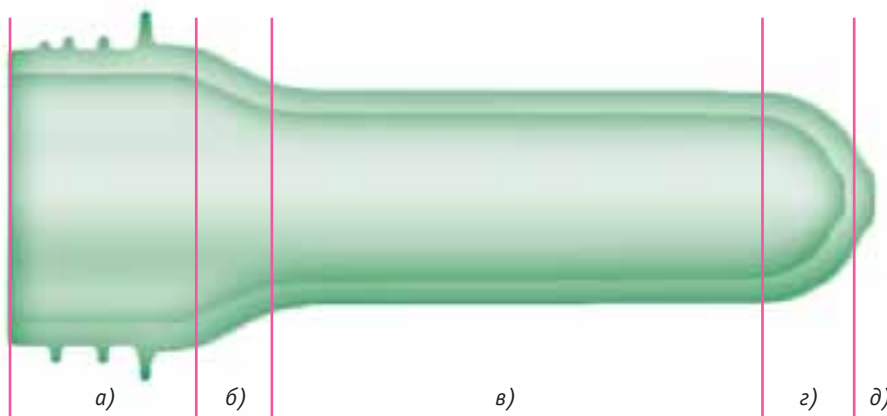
Преформа из ПЭТФ для изготовления бутылки: резьбовая горловина (а); переход от горловины к корпусу (б); корпус (в); дно (г); литник (д)
